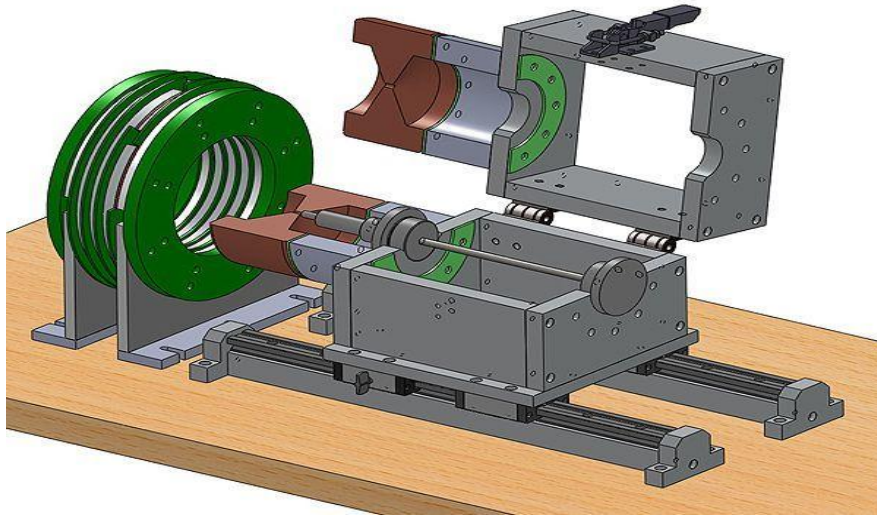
Pièces formées par Soudage électromagnétique
